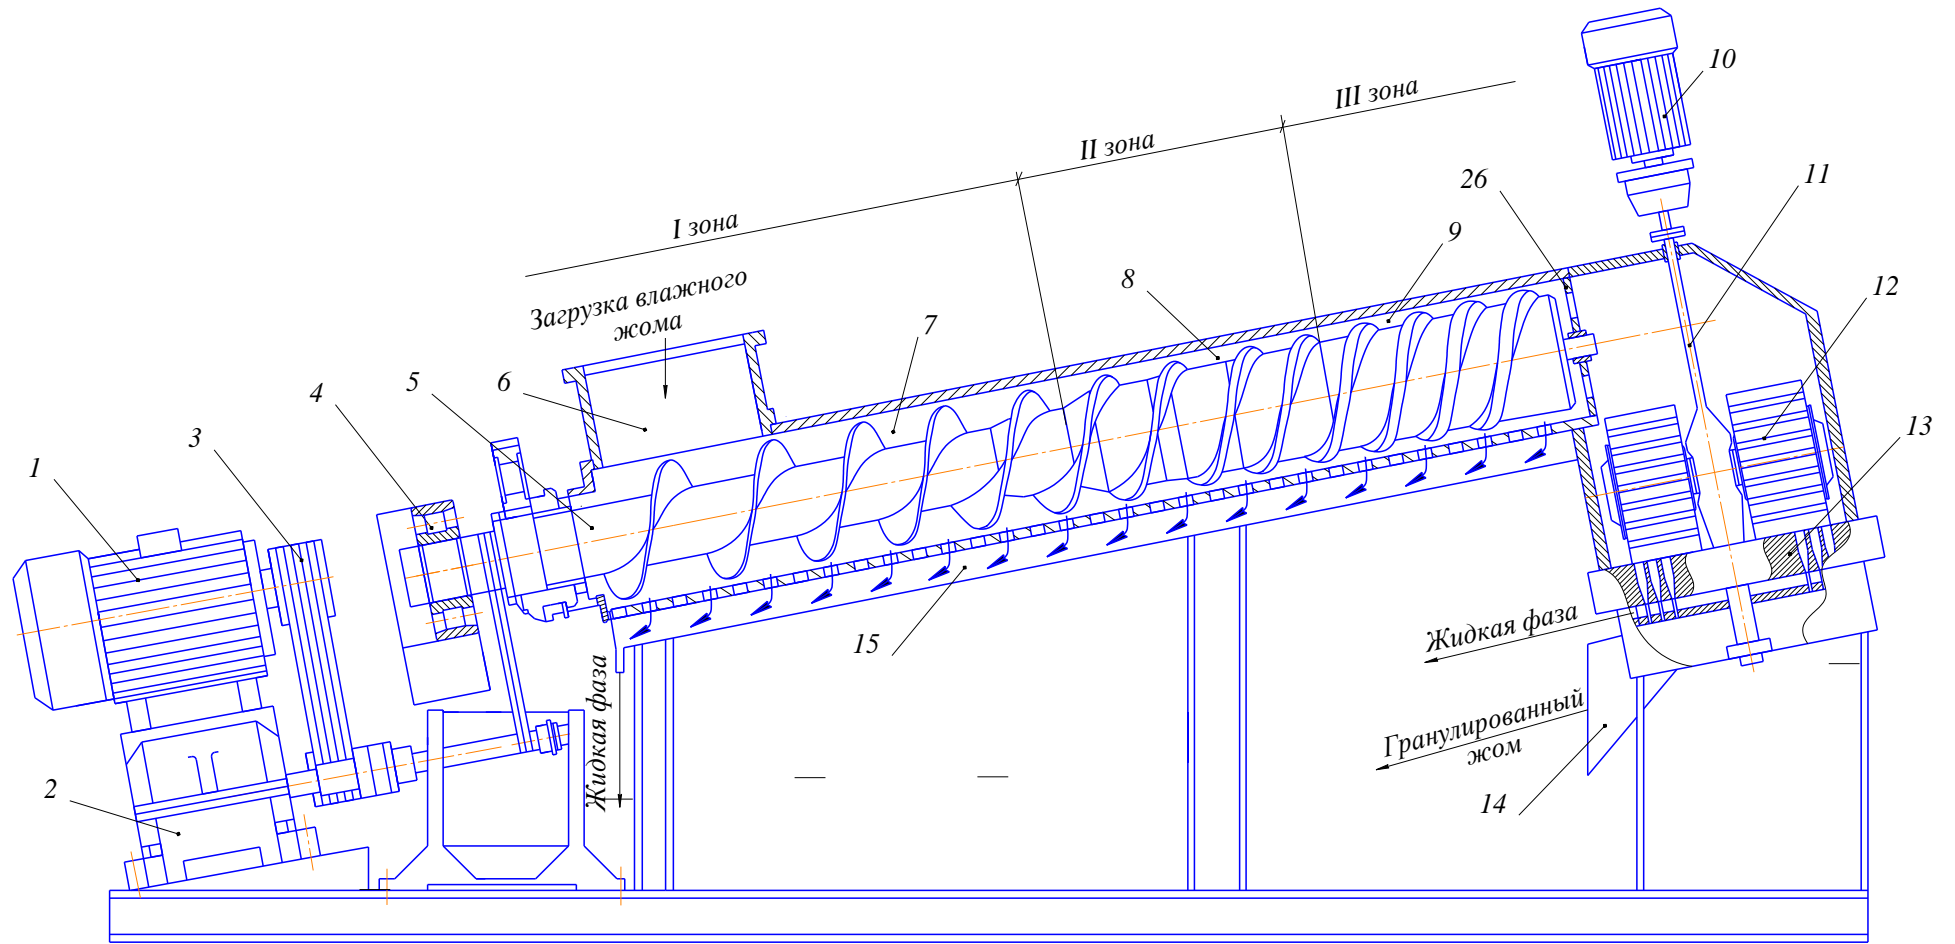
Комбинированный пресс-гранулятор: 1 – электродвигатель, 2 – станина, 3 – ременная передача, 4 – подшипниковая опора, 5 – шнековый вал, 6 – загрузочный бункер, 7, 8, 9 – зоны рабочей камеры наклонного шнекового пресса, 10 – матрица, 11 – привод, 12 – ролики (прессующие вальцы), 13 – плоская матрица, 14 – выгрузочный патрубок для гранулированного жома, 15 – двутельный корпус, 26 – матрица
